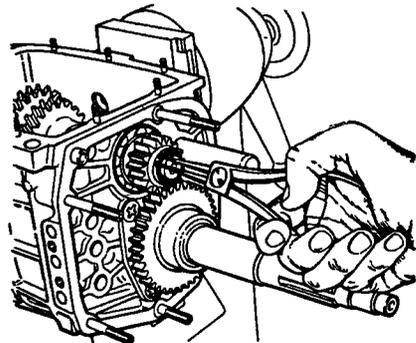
Снятие стопорного пружинного кольца шестерни заднего хода с промежуточного вала
